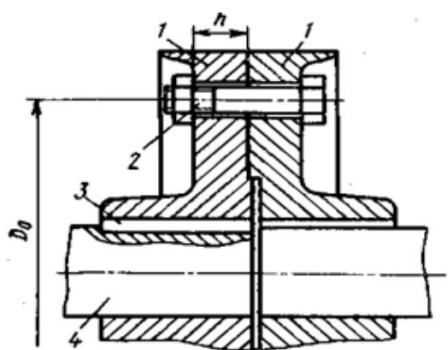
Болтовое соединение дисковой муфты: 1 - полумуфта; 2 - болт; 3 - шпонка; 4 - вал
